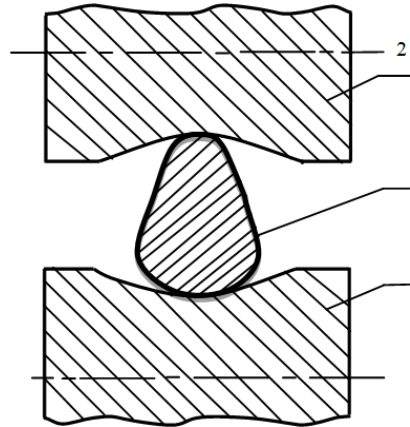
Схема вальцювання криволінійної заготовки в калібрах циліндричних валків:
